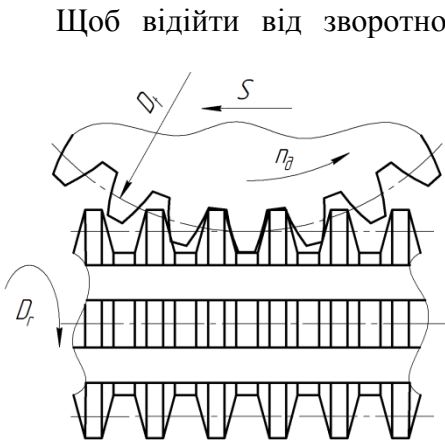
Схема роботи зубонарізної гребінчастої фрези
